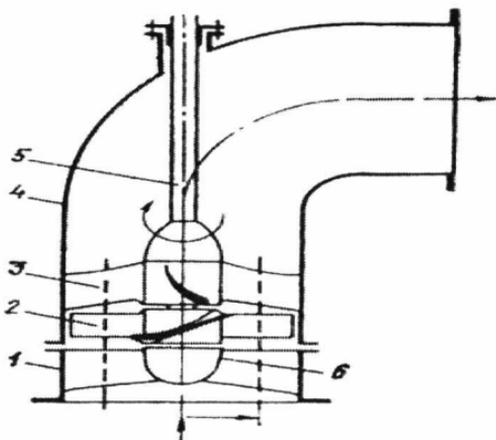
Осевой насос. 1-всасывающий патрубок; 2,3 – лопасти; 4 – напорный патрубок; 5 – вал насоса; 6-штулка.
